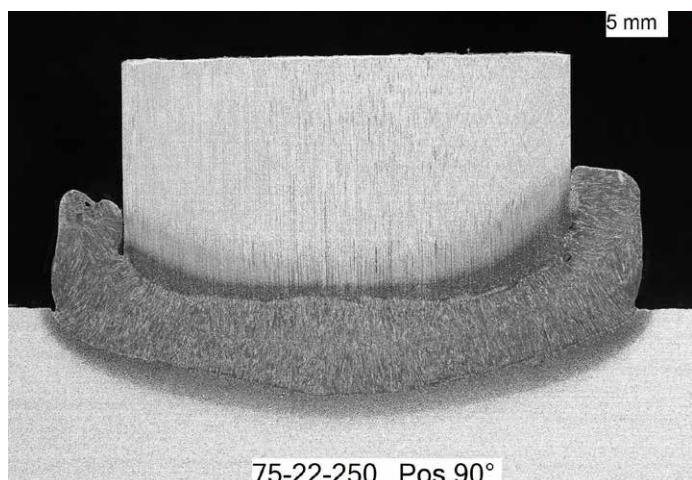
Makroschliff einer einwandfreien Bolzenschweißung mit Keramikring
